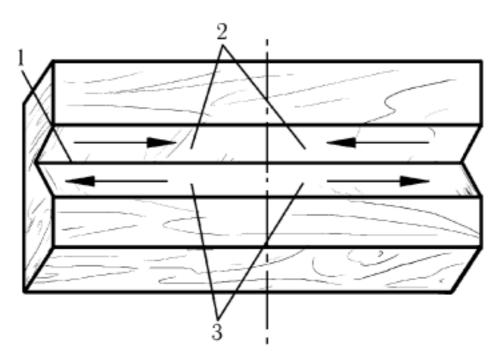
Выполнение прямой двусторонней выемки, направленной вдоль волокон заготовки из свилеватой древесины (стрелками показано направление движения инструмента): 1 – средняя линия; 2, 3 – боковые грани
